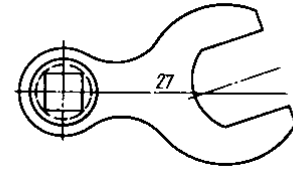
Головка S=17 для регулировки зазоров в клапанах
